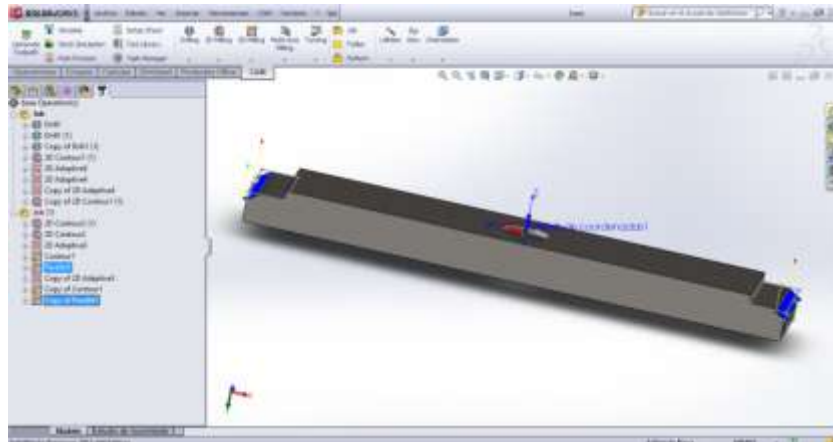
5 Diseño CAM de bancada (maquinado de parte inferior)
